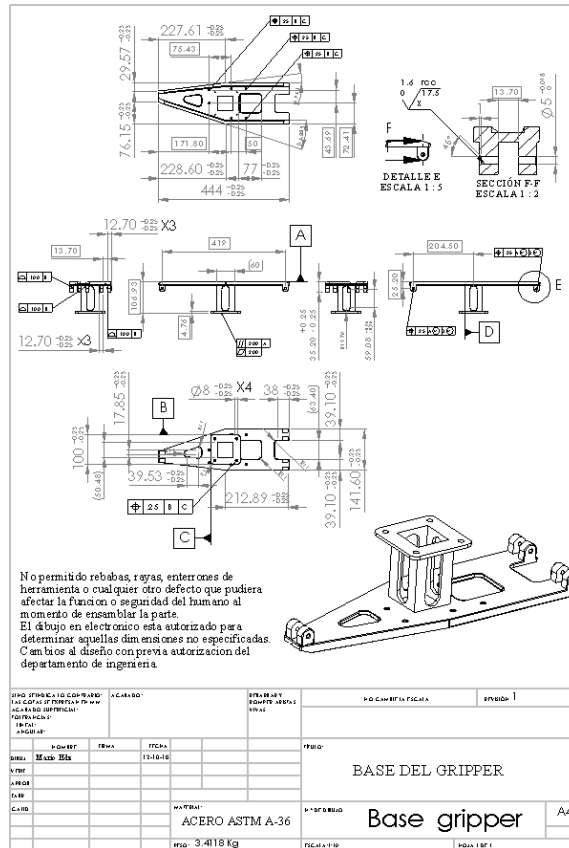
Diseño mecánico de la parte con las especificaciones técnicas.
